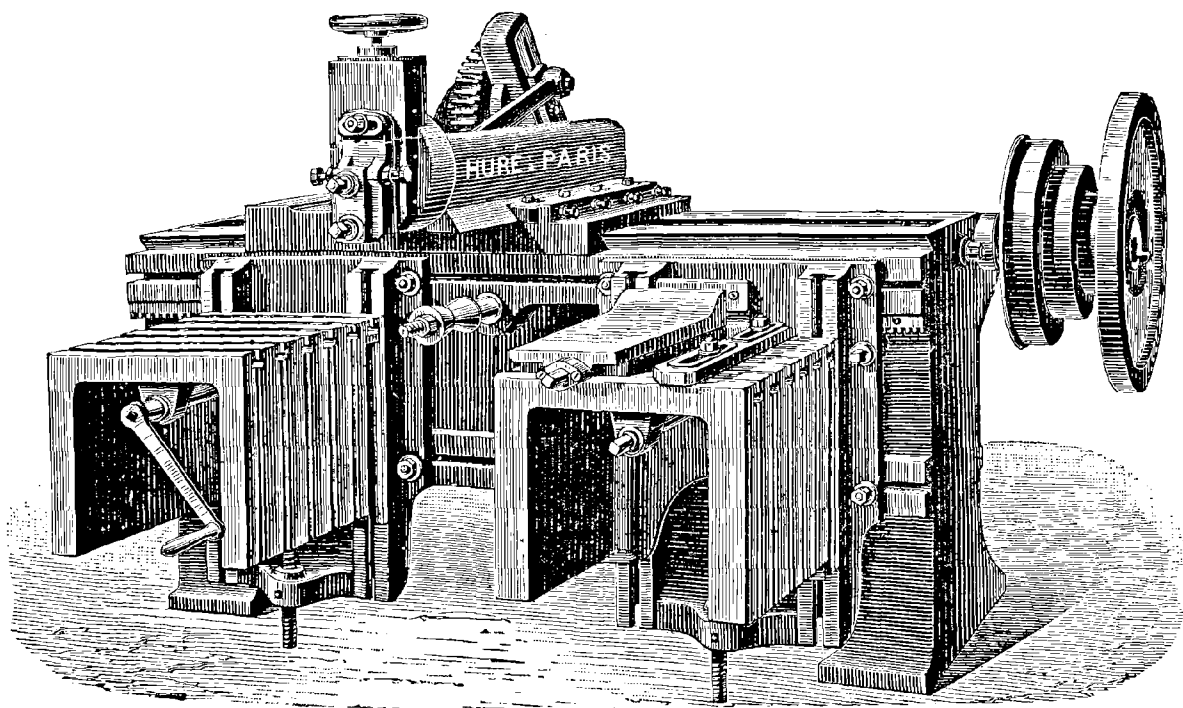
Etau-limeur à double table porte-objet de M. Huré.
